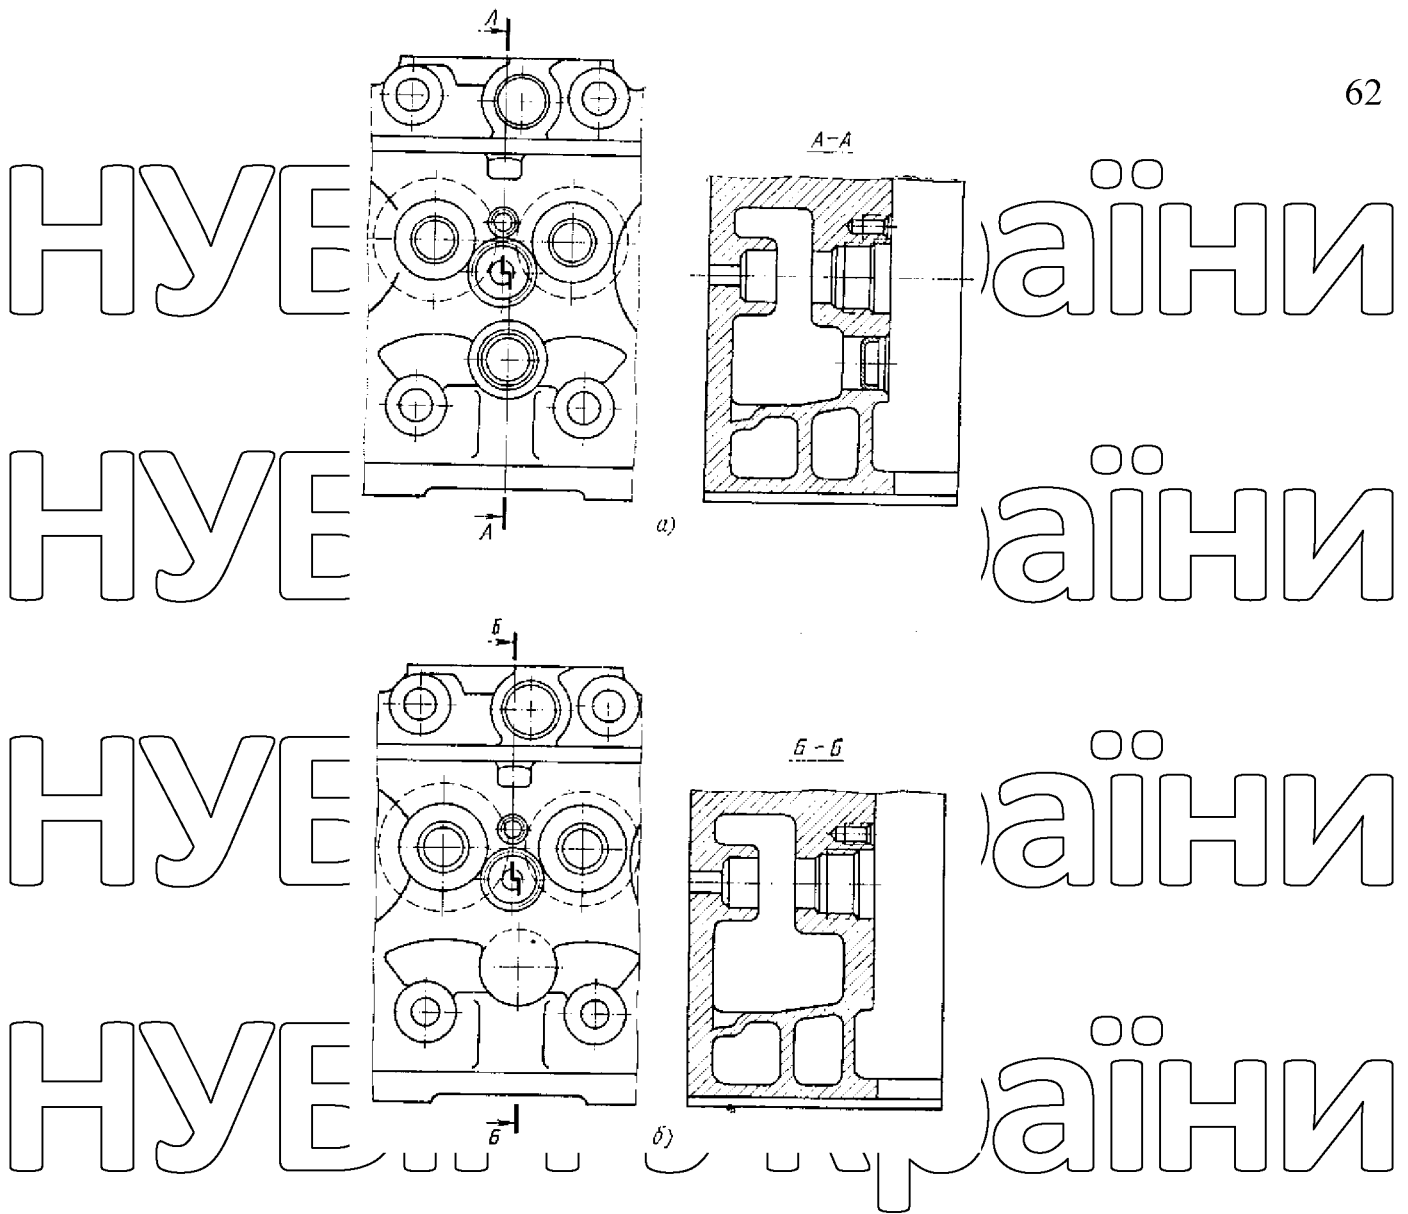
Головка блоку з отвором для ливарного знака на верхній
